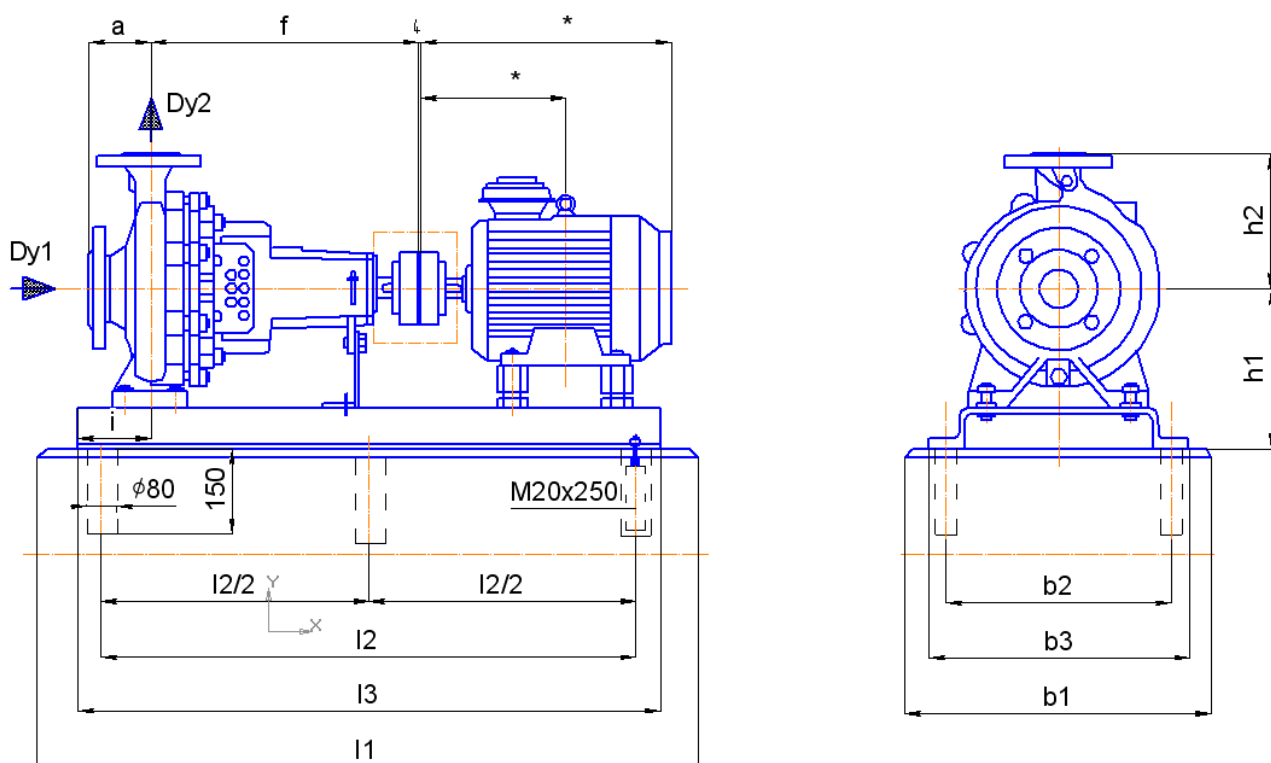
Габаритные и присоединительные размеры Иртыш – ЦНК.
